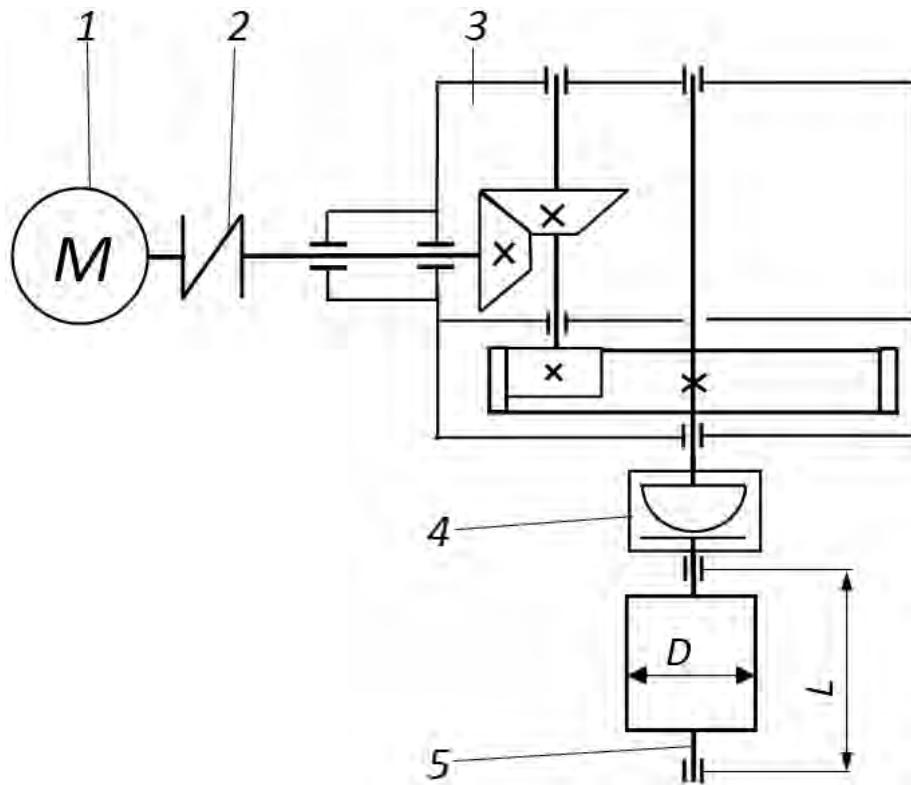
Схема привода ленточного конвейера (вид сверху): 1 – асинхронный электродвигатель; 2 – муфта упругая втулочно-пальцевая; 3 – редуктор коническо-цилиндрический (первая ступень – коническая зубчатая передача с круговым зубом, вторая – цилиндрическая прямозубая зубчатая передача с внутренним зацеплением); 4 – муфта зубчатая; 5 – приводной вал с барабаном
